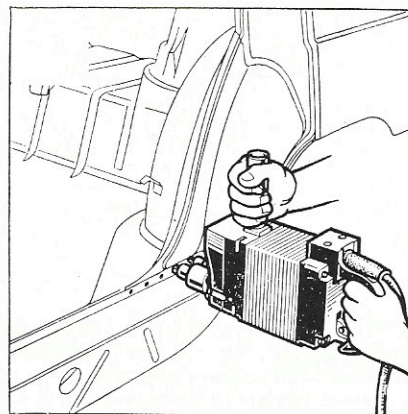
Soudage du longeron extérieur gauche sur passage de roue (partie rectiligne) (double point DP 38). Soudeuse ARO.
